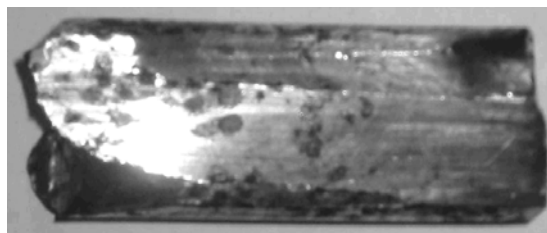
Заготовка из алюминиевого сплава после винтовой экструзии с дефектом (сверху) боковой поверхности
